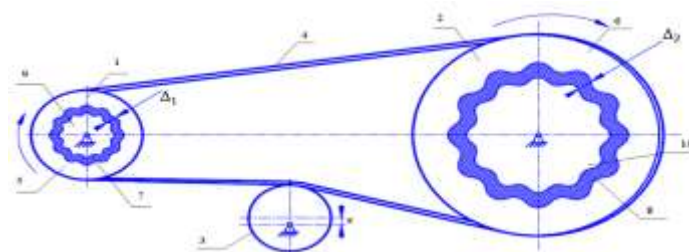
Схема ременной передачи с составными шкивами и эксцентричным натяжным роликом
